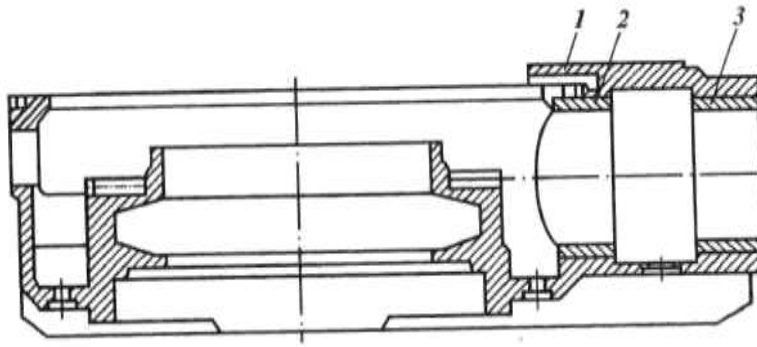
Ремонт станины ротора із застосуванням додаткових ремонтних деталей: 1 - корпус; 2,3 - втулка
